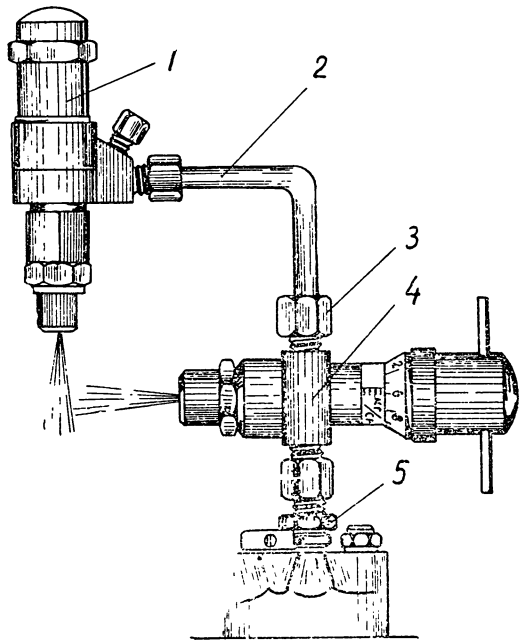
Проверка давления начала впрыска топлива форсункой при помощи максиметра:
